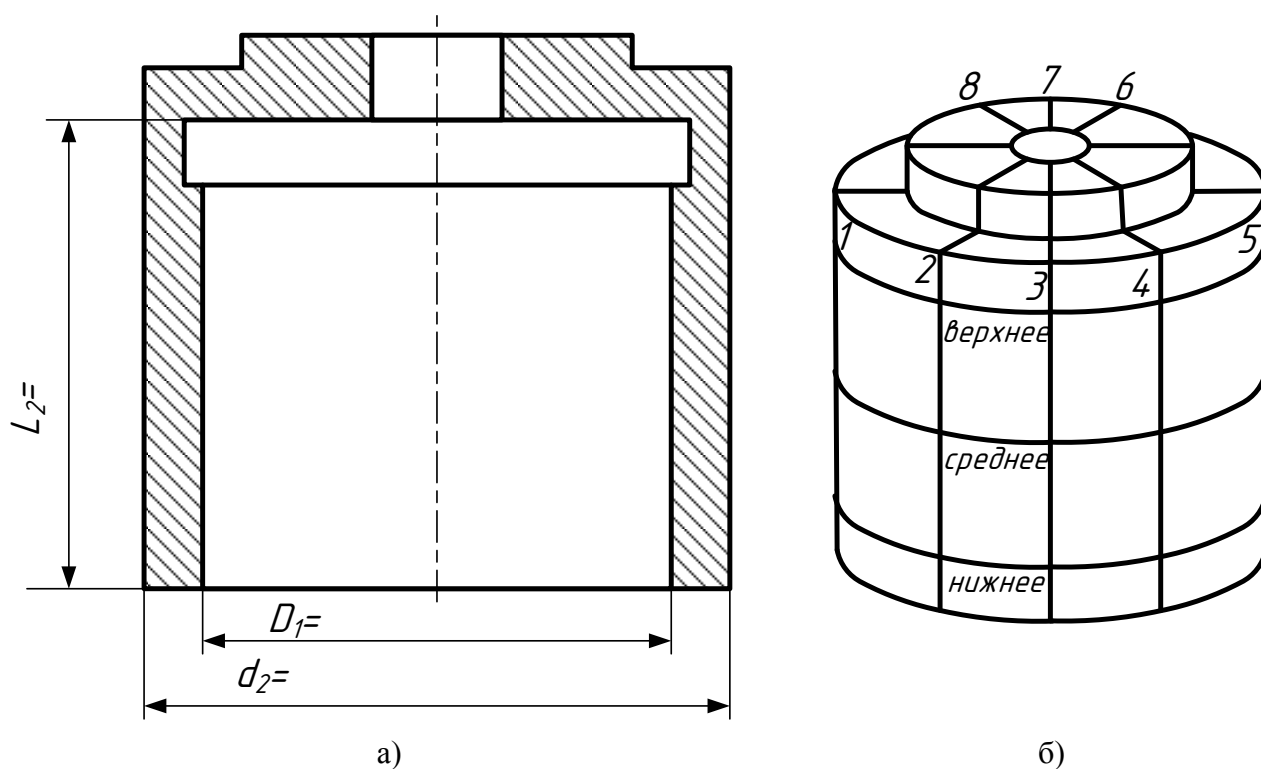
Эскиз измеряемой детали № _____ и схема разбивки детали на сектора
